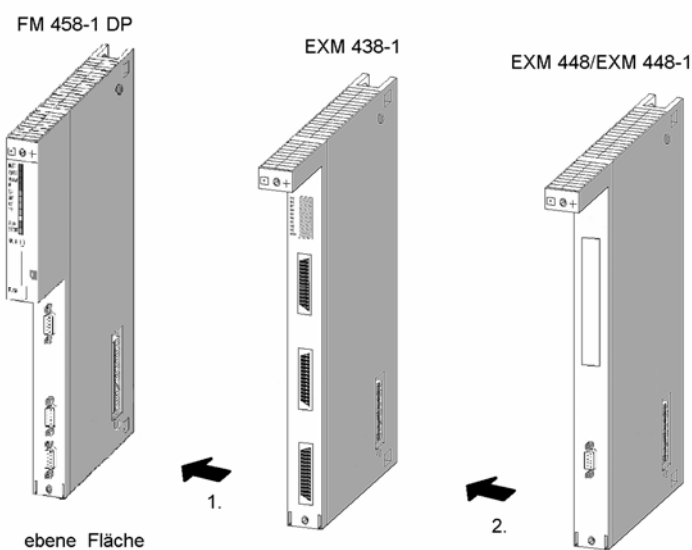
Baugruppen zusammenstecken (Prinzipbild)
